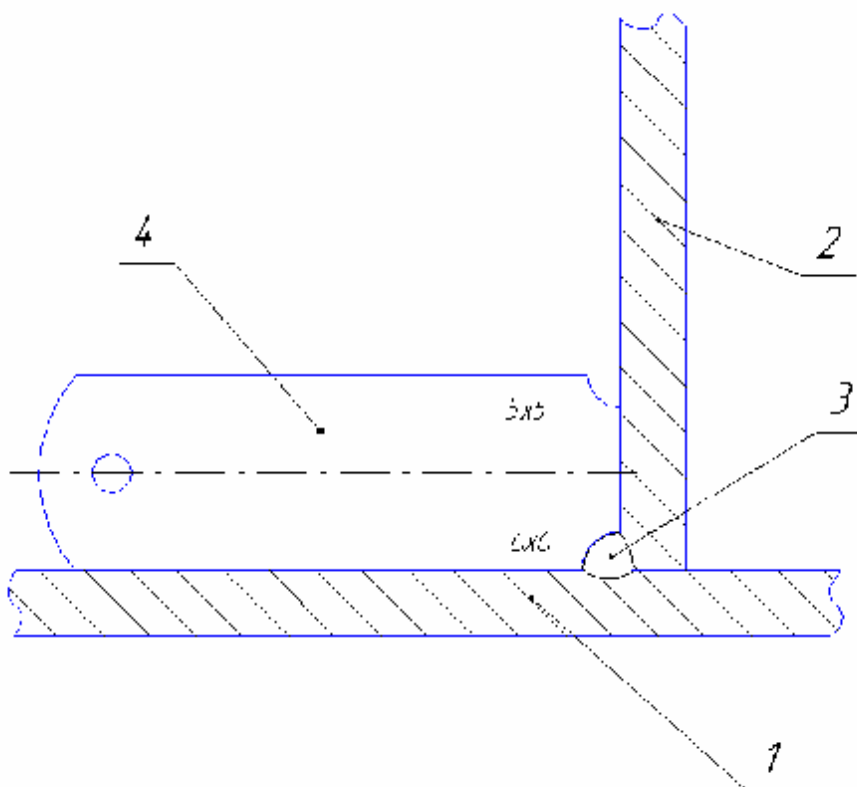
Определение размеров сварного шва с помощью набора катетометров сварщика КМС-3-16
